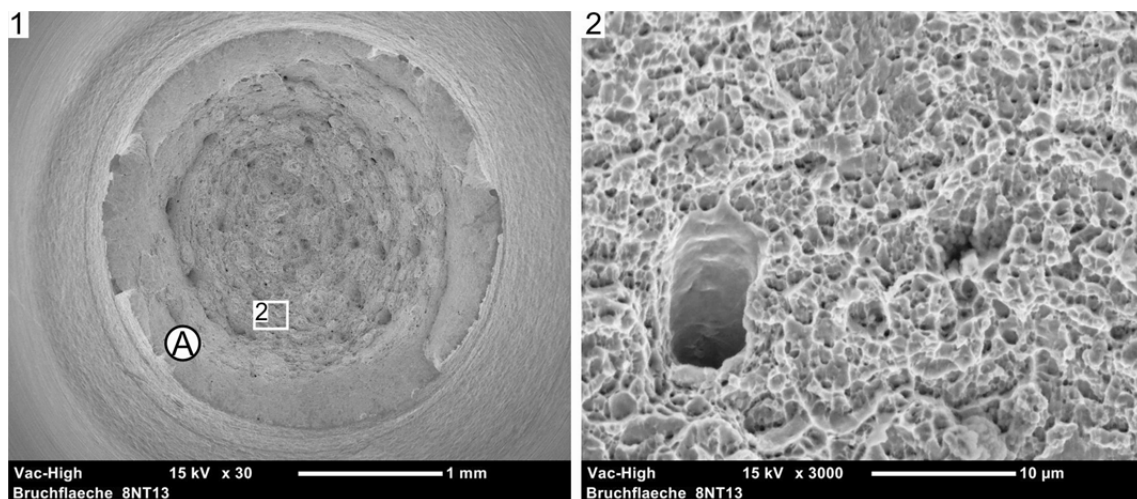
Bruchfläche einer Kerbzugprobe aus der ferritischen WEZ (REM-Aufnahme)
